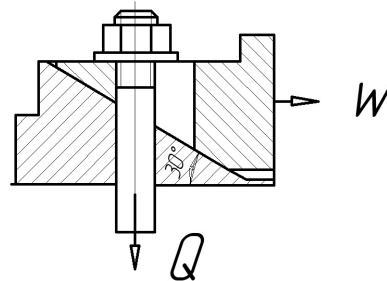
Схема клинового механізму для передавання зусилля затиску
